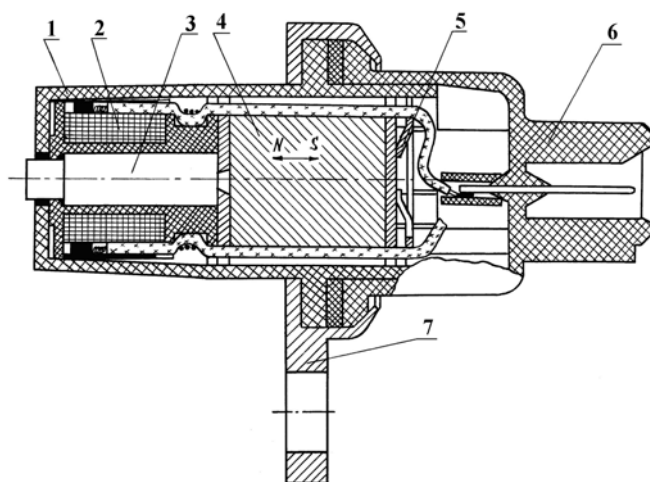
Конструкция типичного индуктивного датчика перемещения: 1 – корпус; 2 – катушка; 3 – сердечник; 4 – постоянный магнит из феррита бария; 5 – кольцо пружинное; 6 – разъем датчика со штекерами; 7 – фланец крепления датчика
